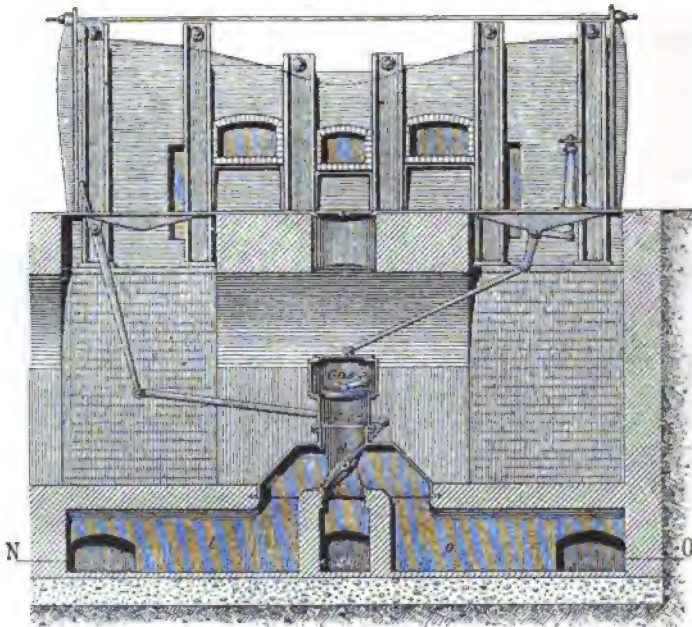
Ofen mit Siemens' Gasfeuerung. Querschnitt durch die Gaskanäle.
